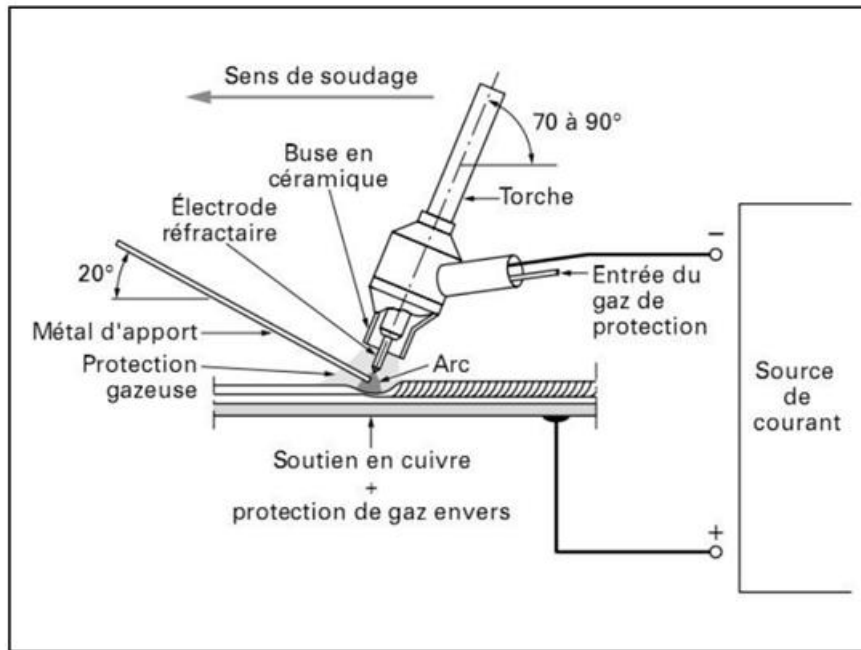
Principe du soudage à l'électrode réfractaire TIG manuel [11].
